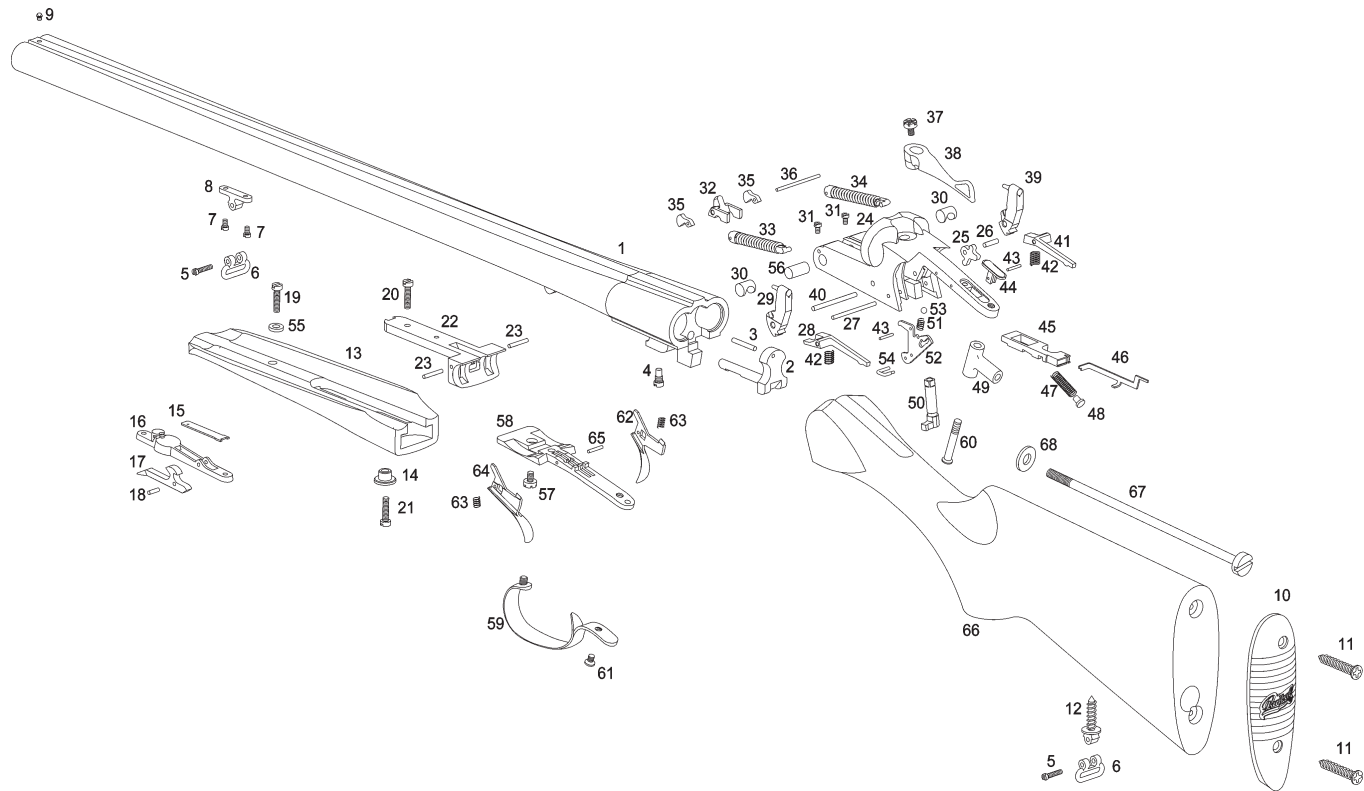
Сборочные единицы и детали ружья МР-43
